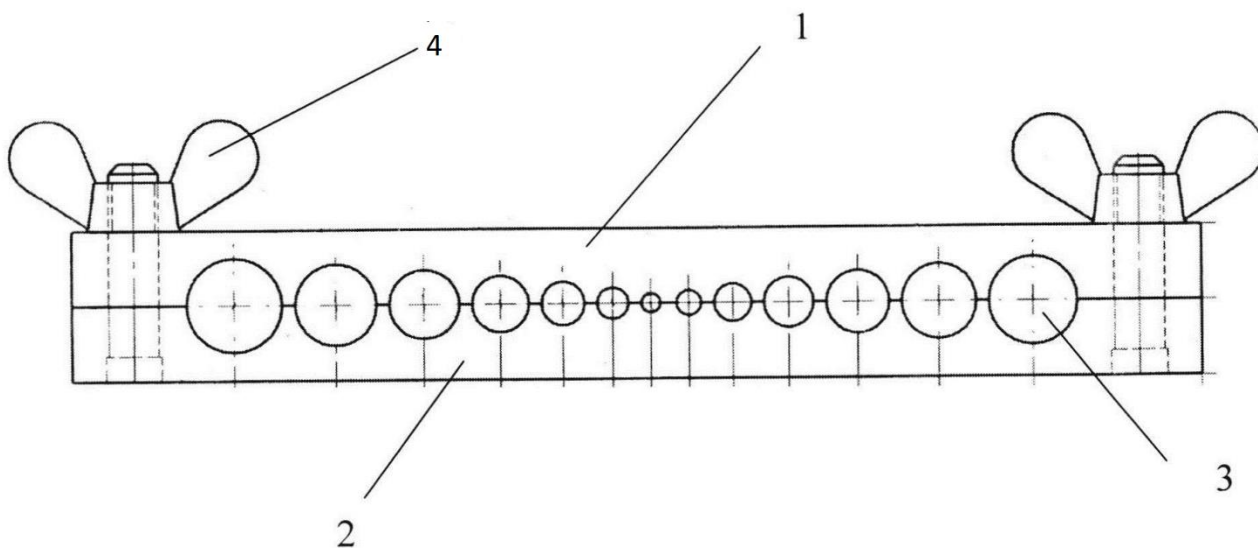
Схема пресс-формы: 1- верхняя плита, 2 – нижняя плита, 3 – каналы плит полуцилиндрической формы, 4 – гайки-барашки для соединения плит между собой.
